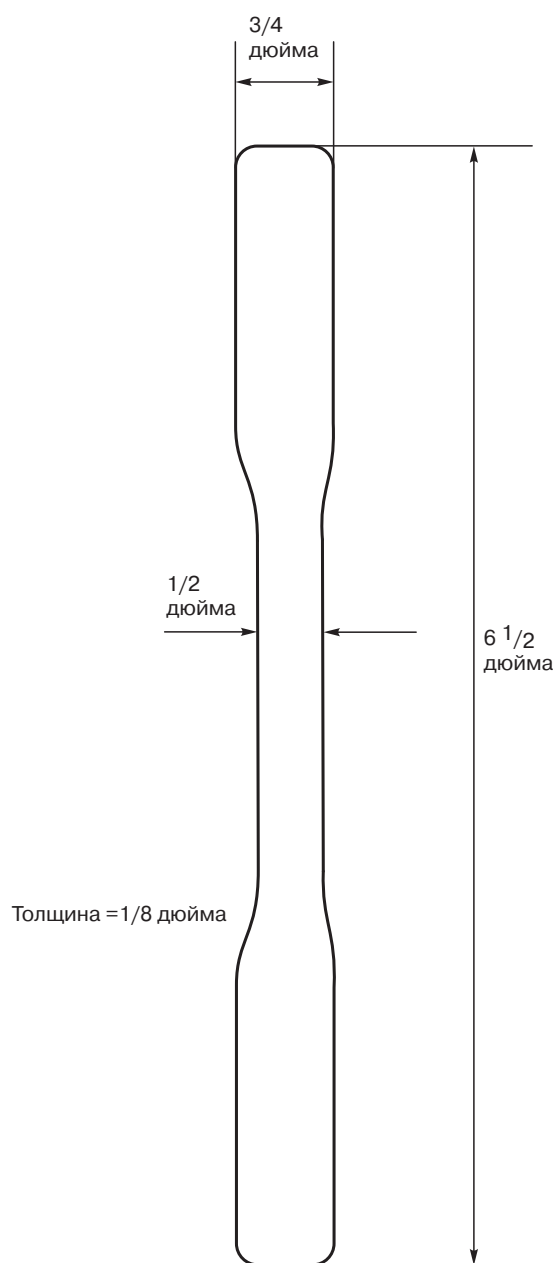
Стандартный образец для испытаний на растяжение (тип I)
